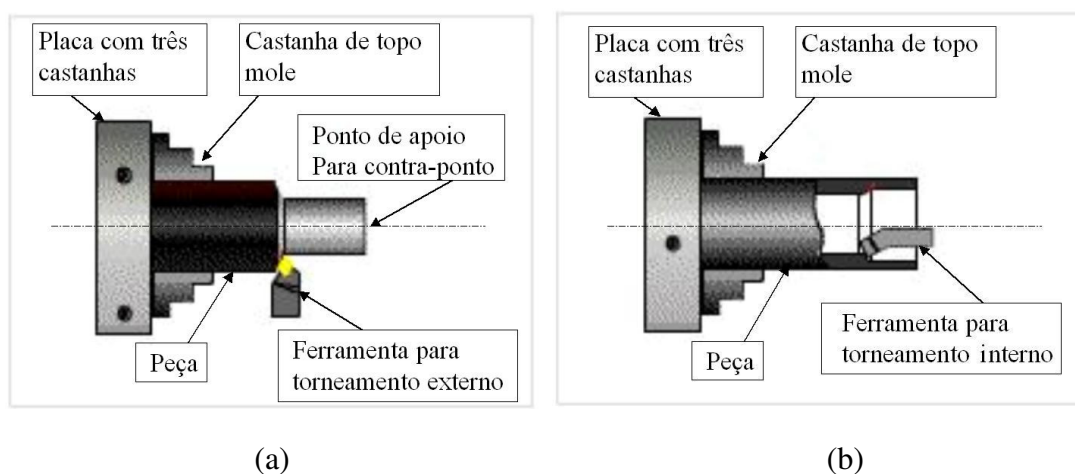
Ilustrações de torneamento. (a) cilíndrico externo e (b) torneamento cilíndrico interno, adaptado de [4].
